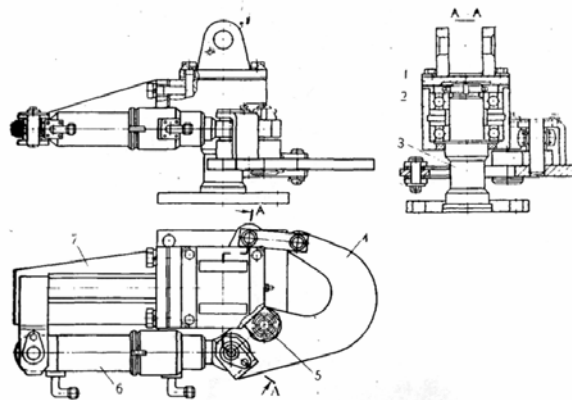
Поворотная головка ковша грейфера экскаваторов ЭО-4124А и ЭО-4125:
